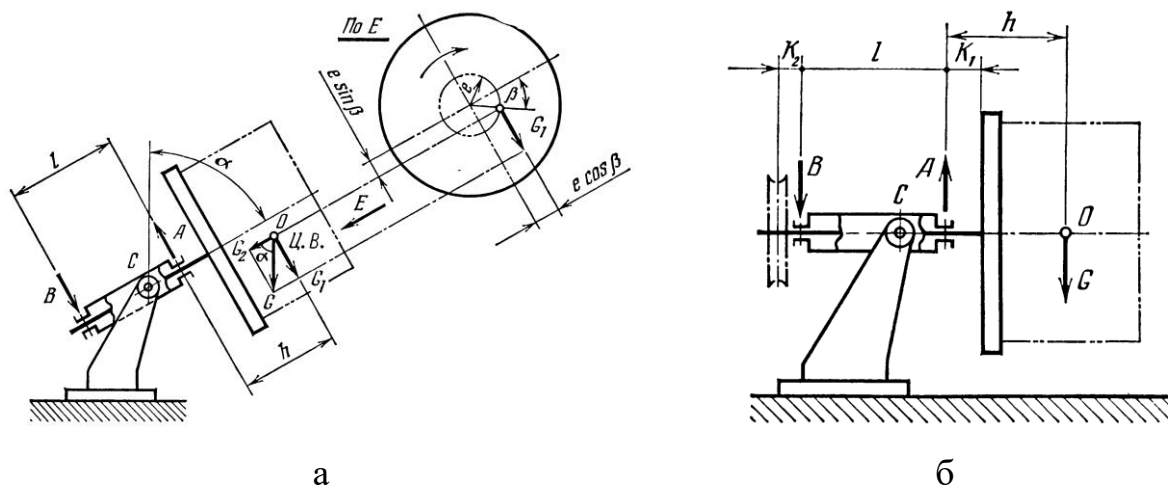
Розрахункова схема механізму обертання УЗО:
